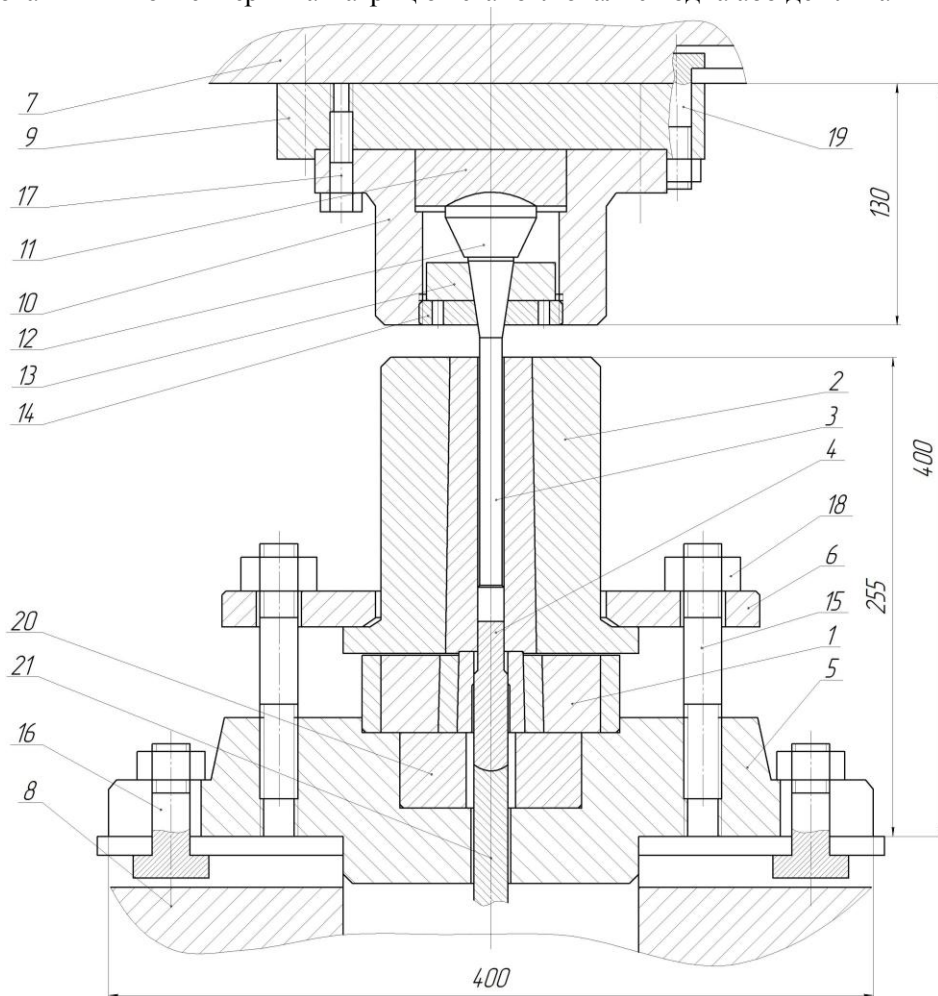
Загальний вигляд штамп для прямого видавлювання з роздачею профілів з круглих заготовок.
